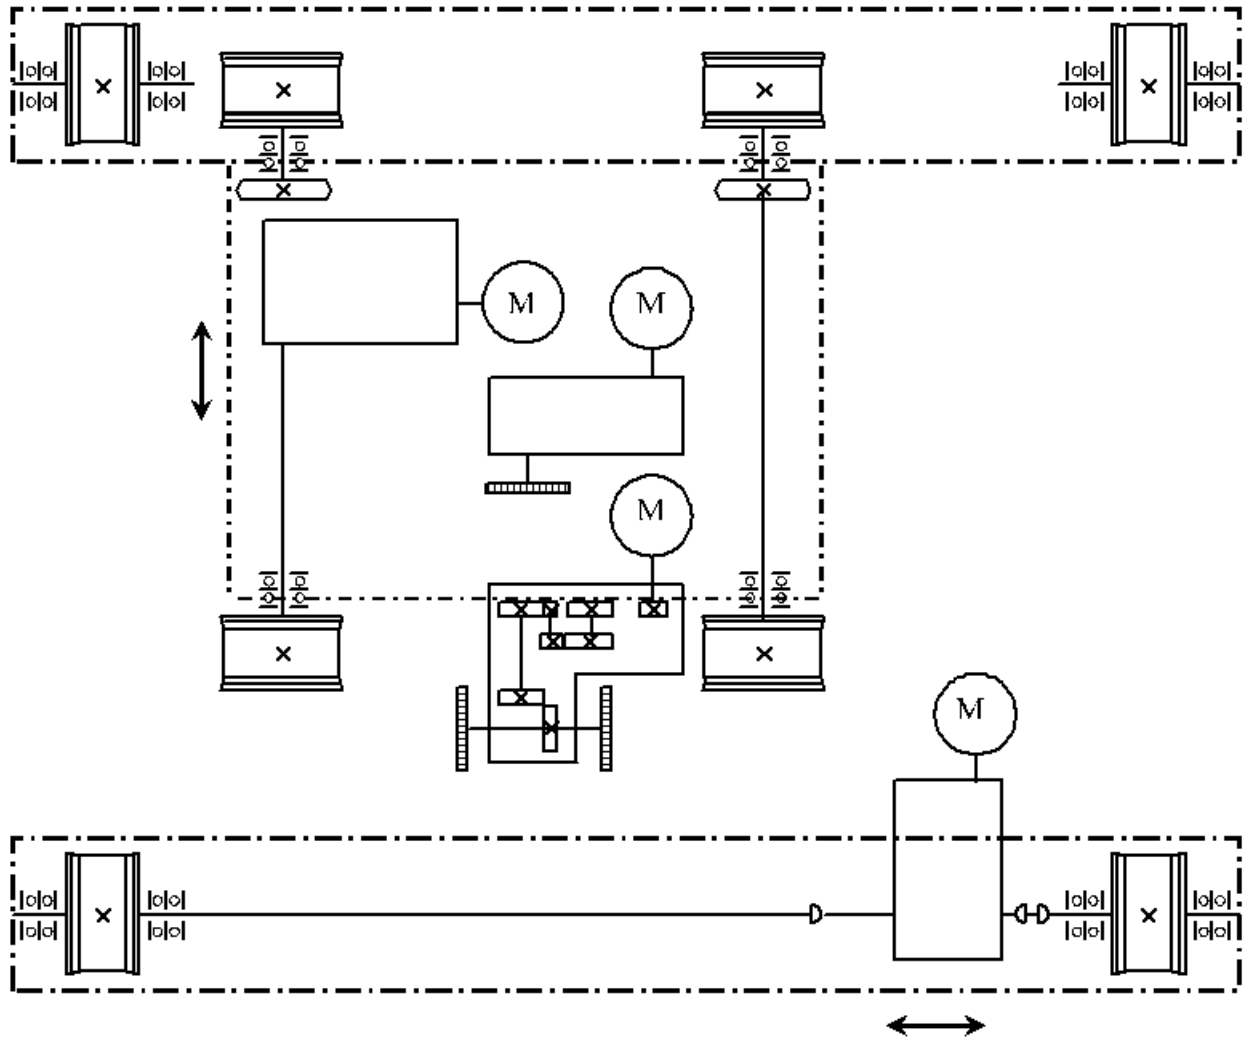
Кінематична схема каменерізної машини СМ-89А. Позначено: 1 – коробка передач механізму переміщення основної рами; 2 – привод горизонтальних пил; 3 – коробка передач верхнього візка; 4 – редуктор привода вертикальних пил.
